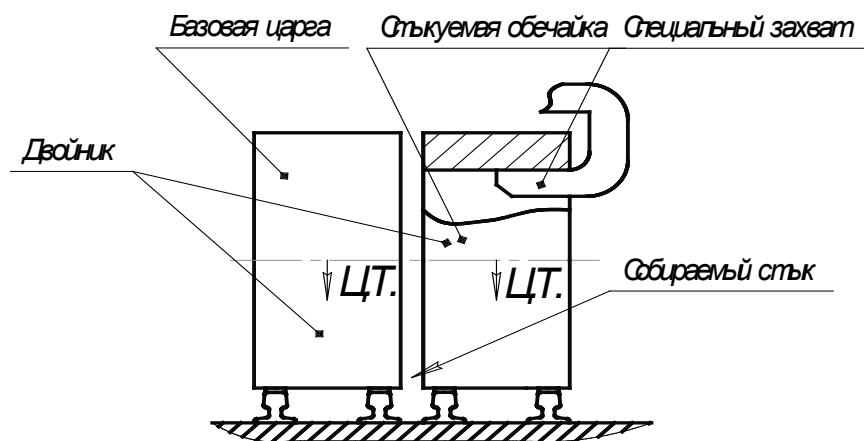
Схема установки стыкуемой обечайки к базовой при сборке двойника
